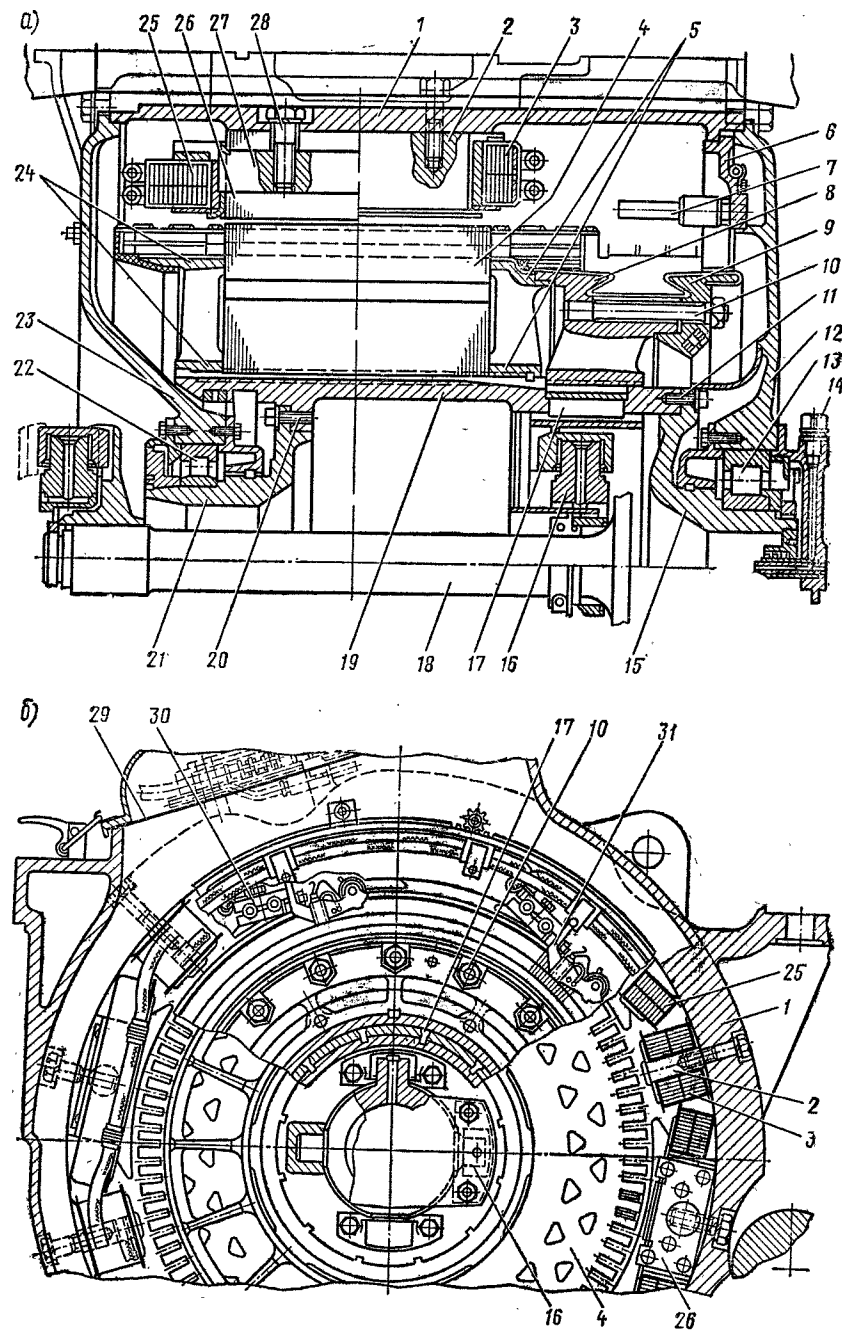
Продольный (а) и поперечный (б) разрезы тягового двигателя AL-4846Г
